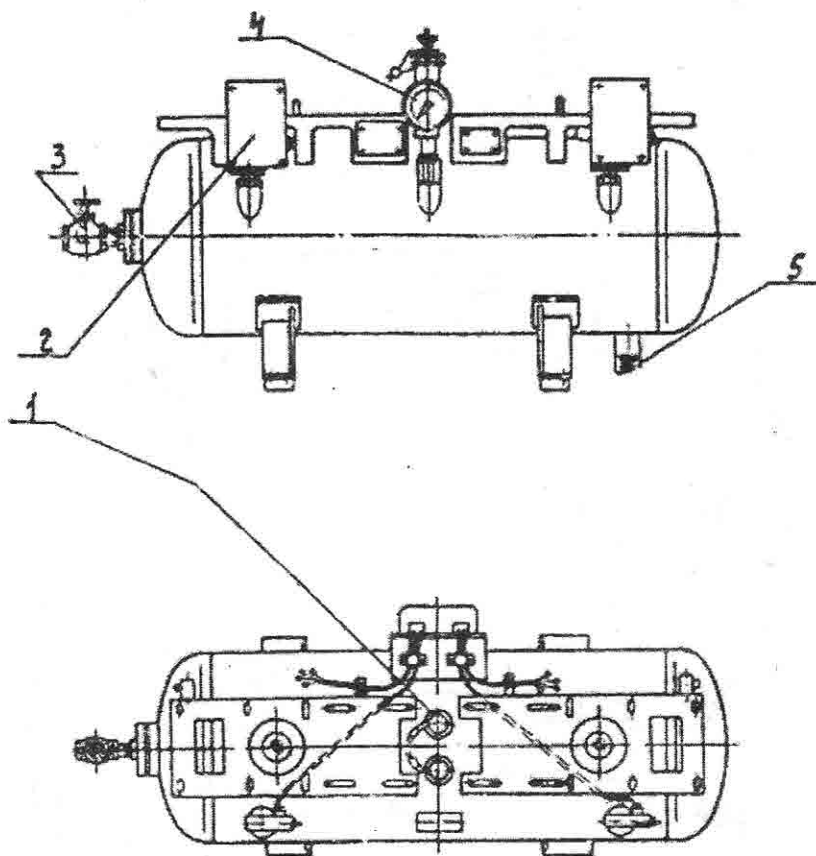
Ресивер установки компрессорной, модель К-3, К-20, К-30:
